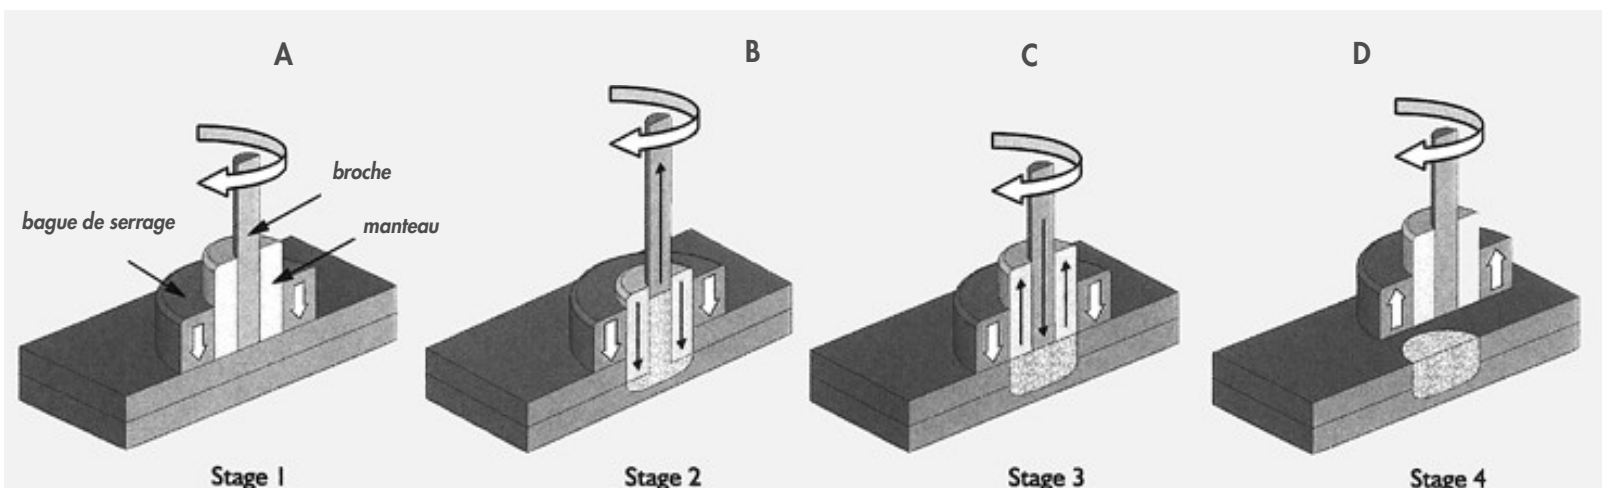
principe de fonctionnement du soudage par points par friction [1,2]
